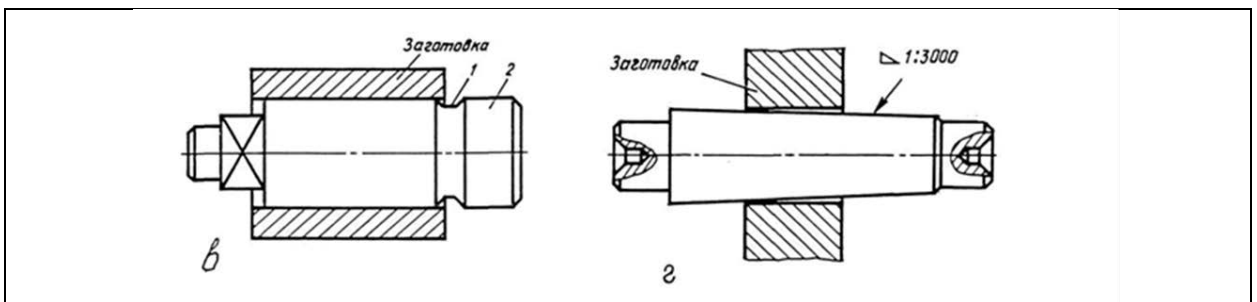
Установлення заготовок на жорсткі циліндричні оправки: в- з гарантованим натягом; г-на конічну оправку
